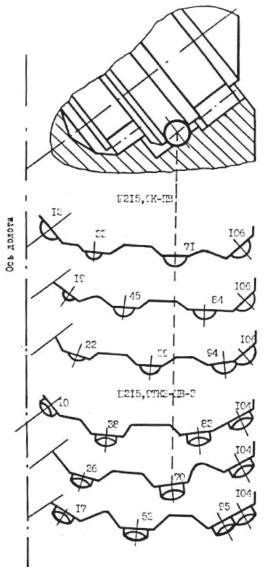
Схема опорного узла шарошки и схема поражения забоя исследуемыми долотами
